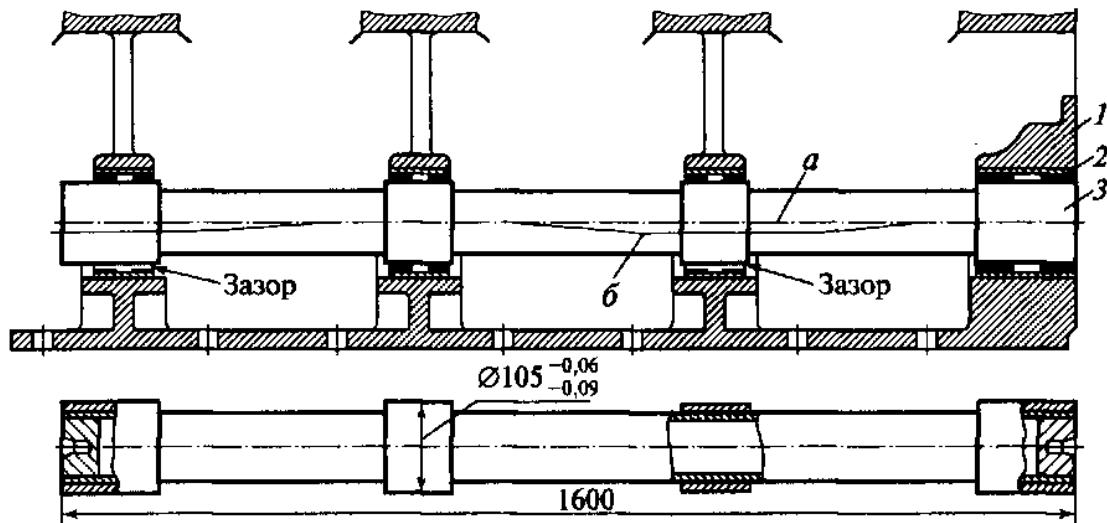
Технологический вал для проверки соосности и ступенчатости подшипников распределительного вала дизеля Д50:
